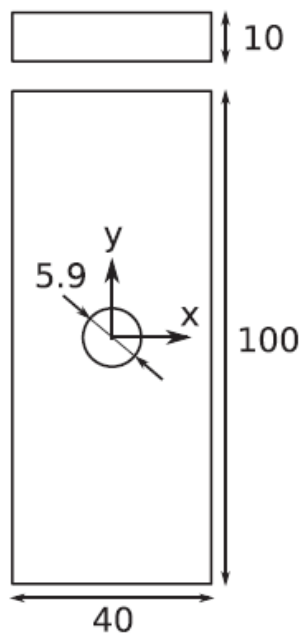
Géométrie de l'éprouvette (dimension en mm).
